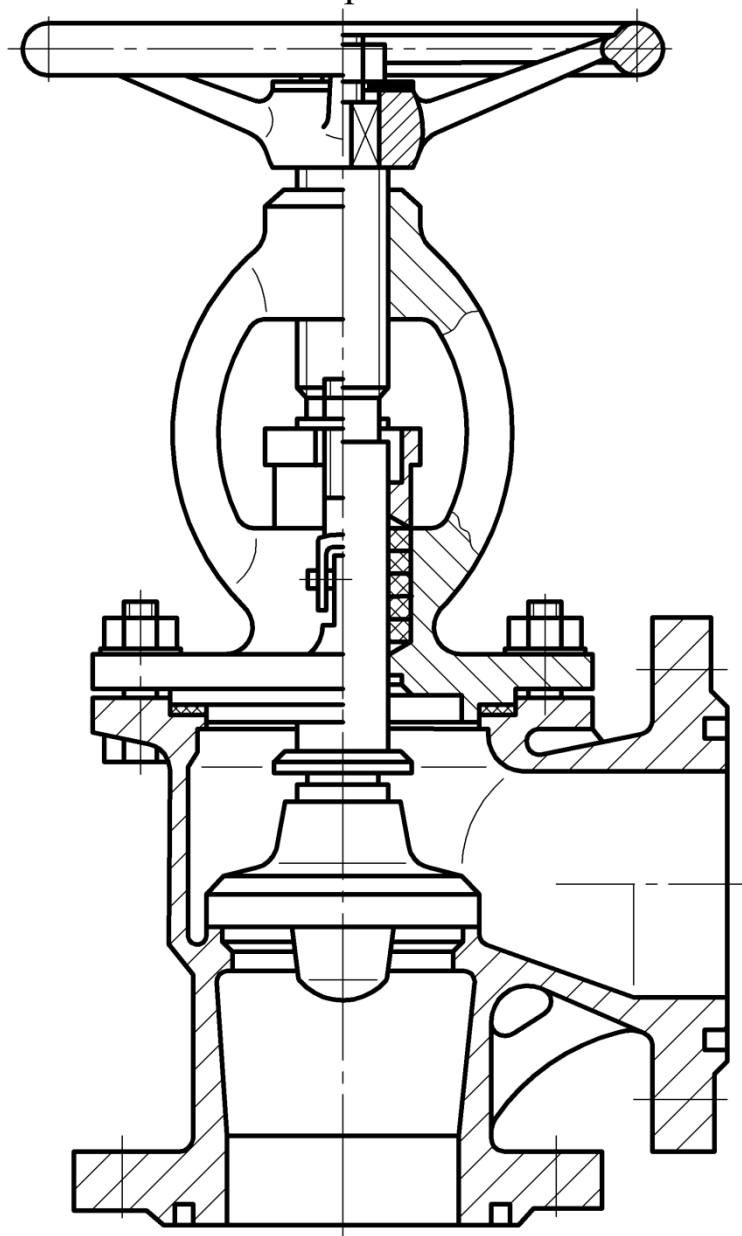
Пример оформления сборочного чертежа задвижки
